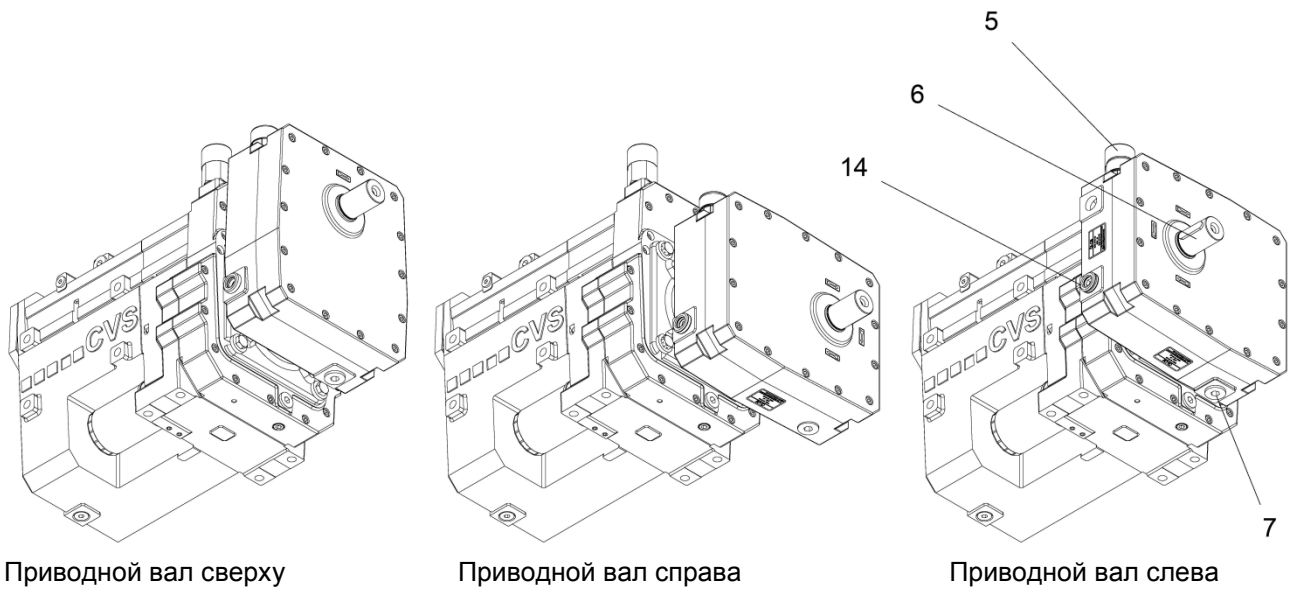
Общий вид SiloKing типа LS с редуктором привода
